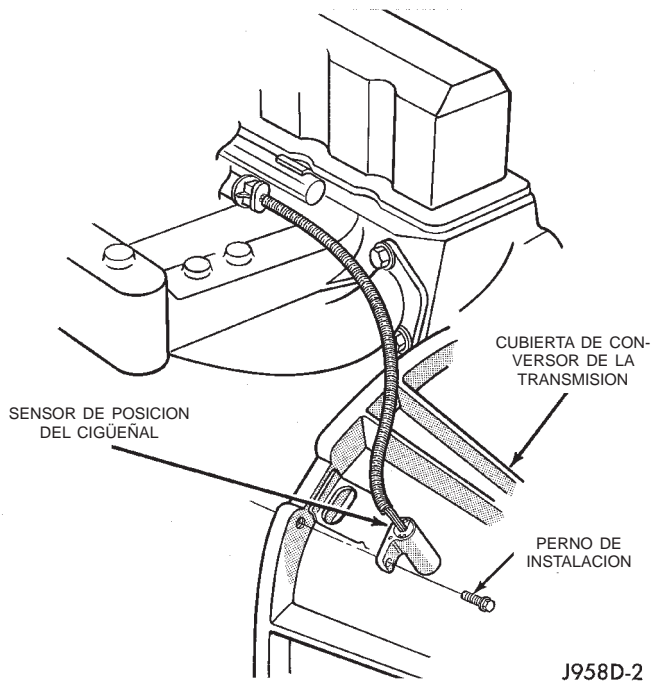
Sensor de posición del cigüeñal—Motor 4.0L
